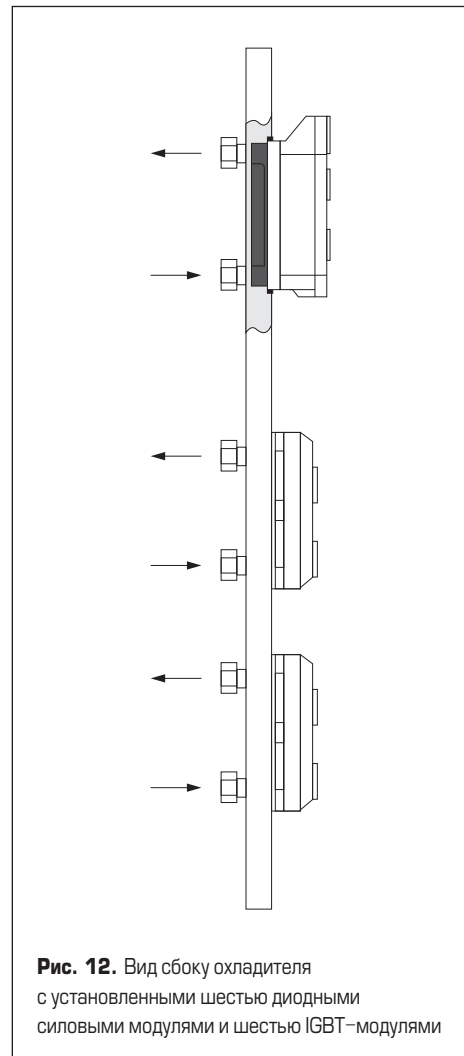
Вид сборки охладителя с установленными шестью диодными силовыми модулями и шестью IGBT-модулями
